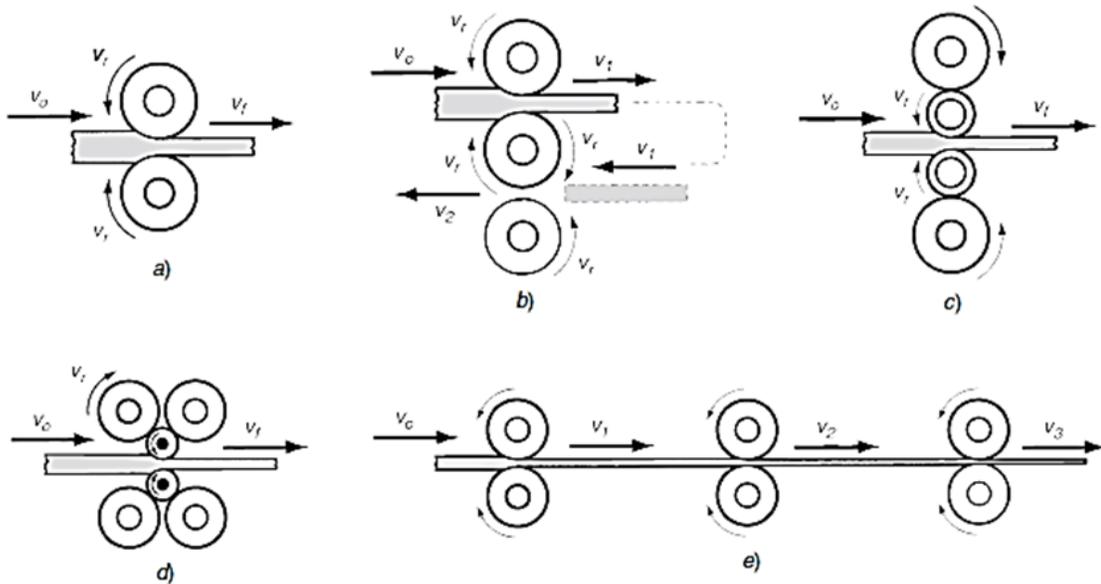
Varias configuraciones de molinos de laminación: a) dos rodillos, b) tres rodillos, d) molino en conjunto y e) molino de rodillos en tándem
